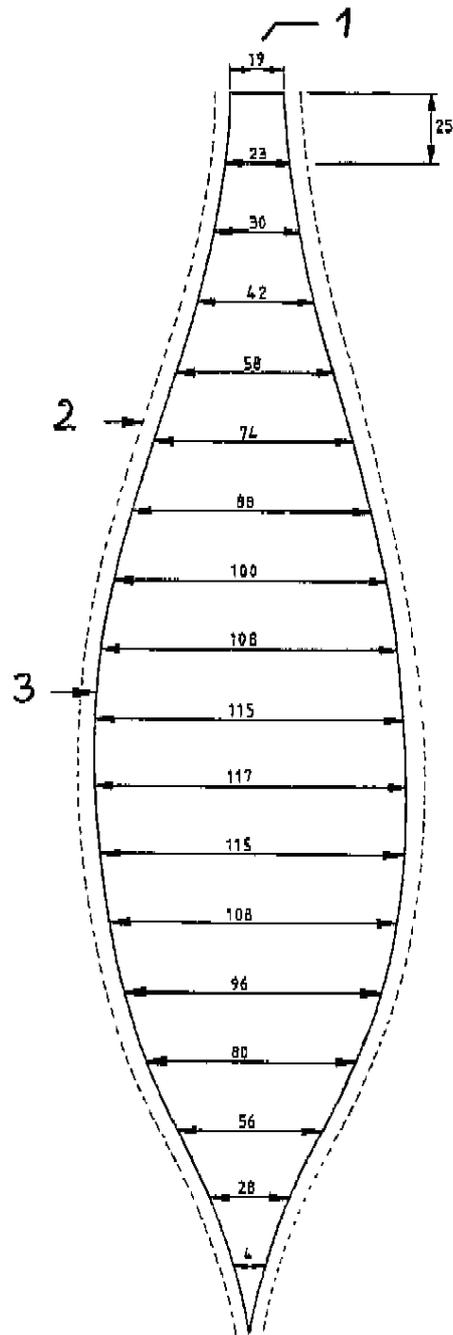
Einspannen des Probekörpers (Schnitt A - A von Bild 3)
